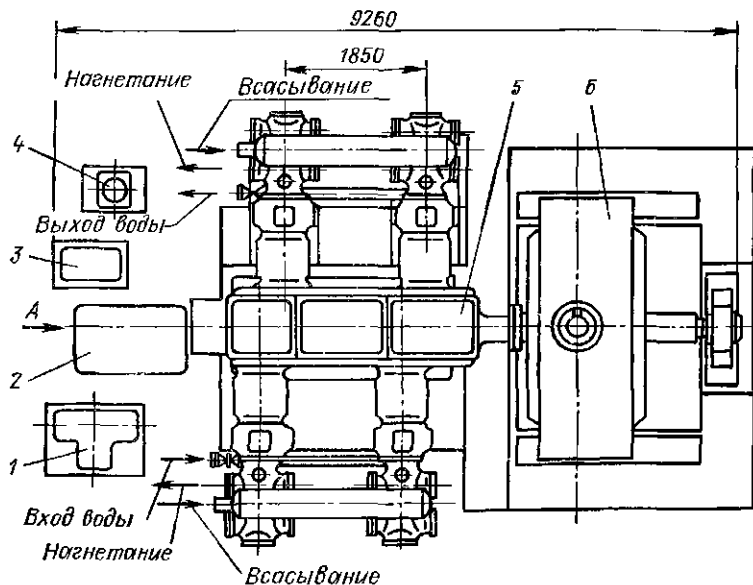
Компрессорная установка с компрессором 4ГМ16-45/35-55СМ2
